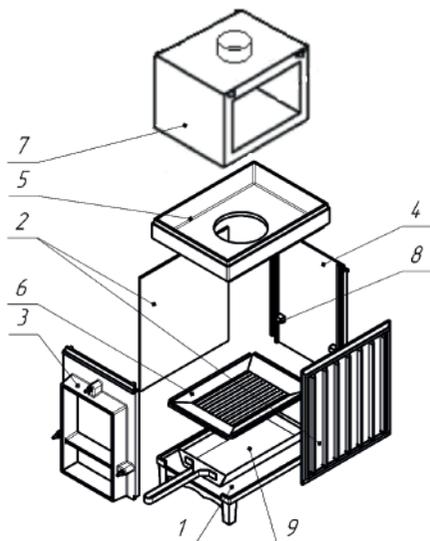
Схема сборки топочного агрегата печи Сударушка М.
